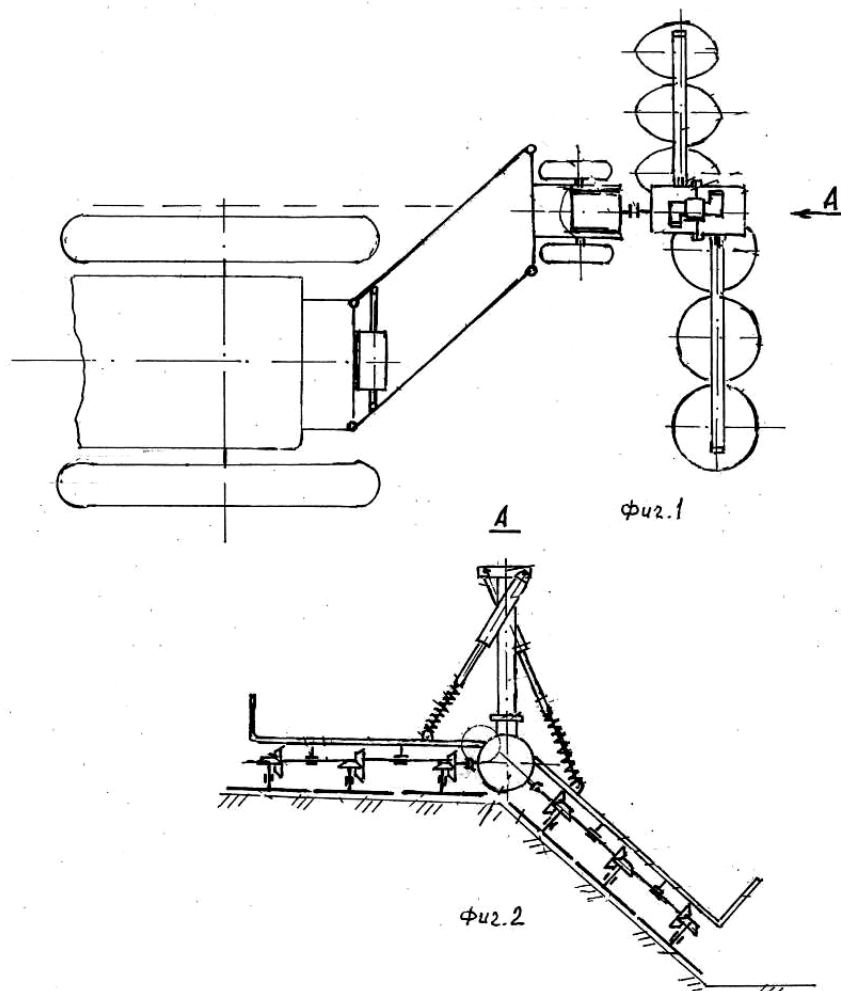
Схема общего вида косилки (фиг. 1, вид сверху) и вид косилки сзади (фиг. 2)
